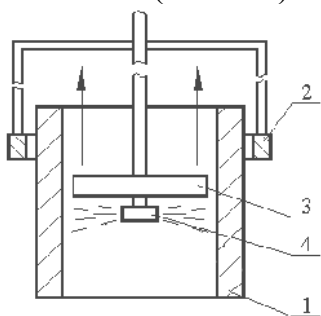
Схема предложенного способа термообработки гильз цилиндров
